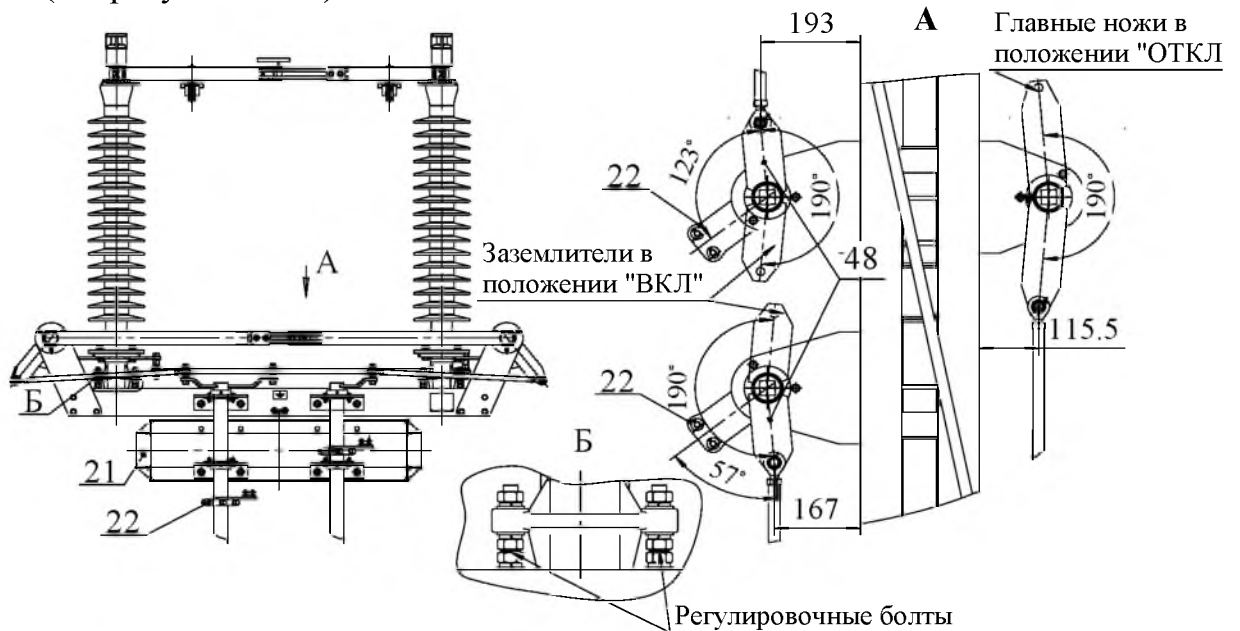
Общий вид ступенчато-килевого разъединителя РН□СК СЭЩ®
